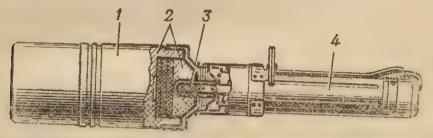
Устройство ручной противотанковой кумулятивной гранаты РКГ-3: 7 — жорпус; 2 — разрывной заряд; 3 — запал; 4 — рукоятка
